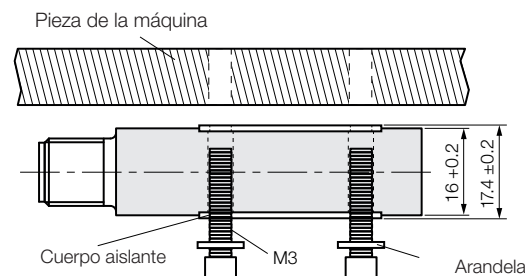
Montaje de la cabeza de sensor con cuerpo aislante
